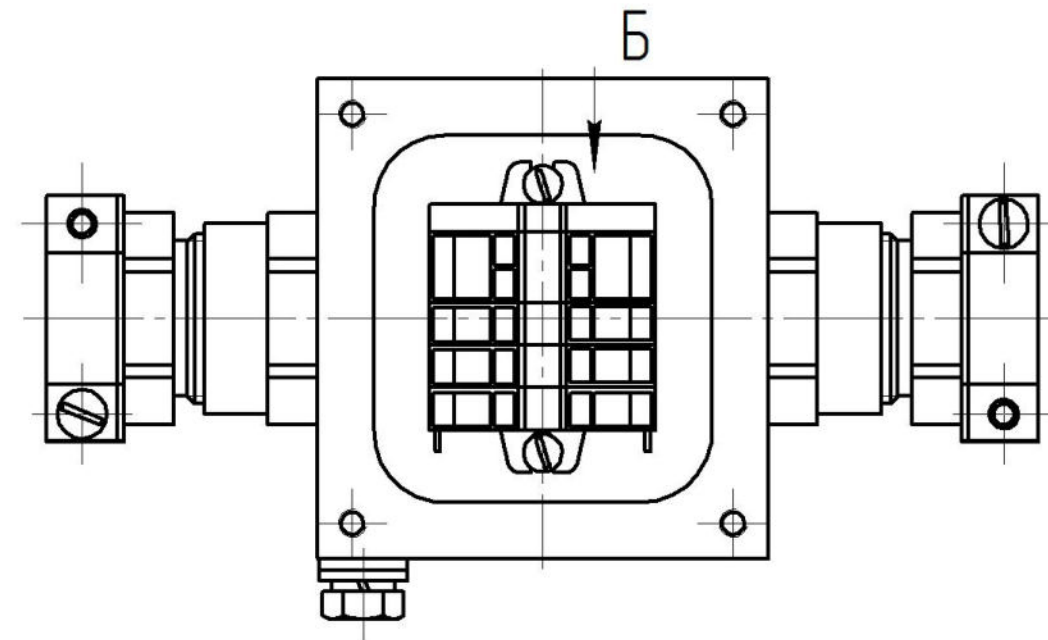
Внешний вид и присоединительные размеры коробки КСВ-5-6-3
